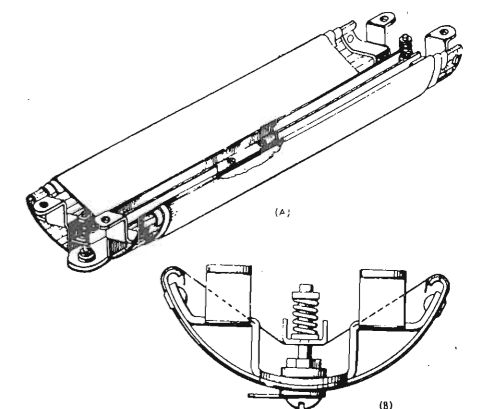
Sezione e vista assonometrica dell'altoparlante elettrostatico.
